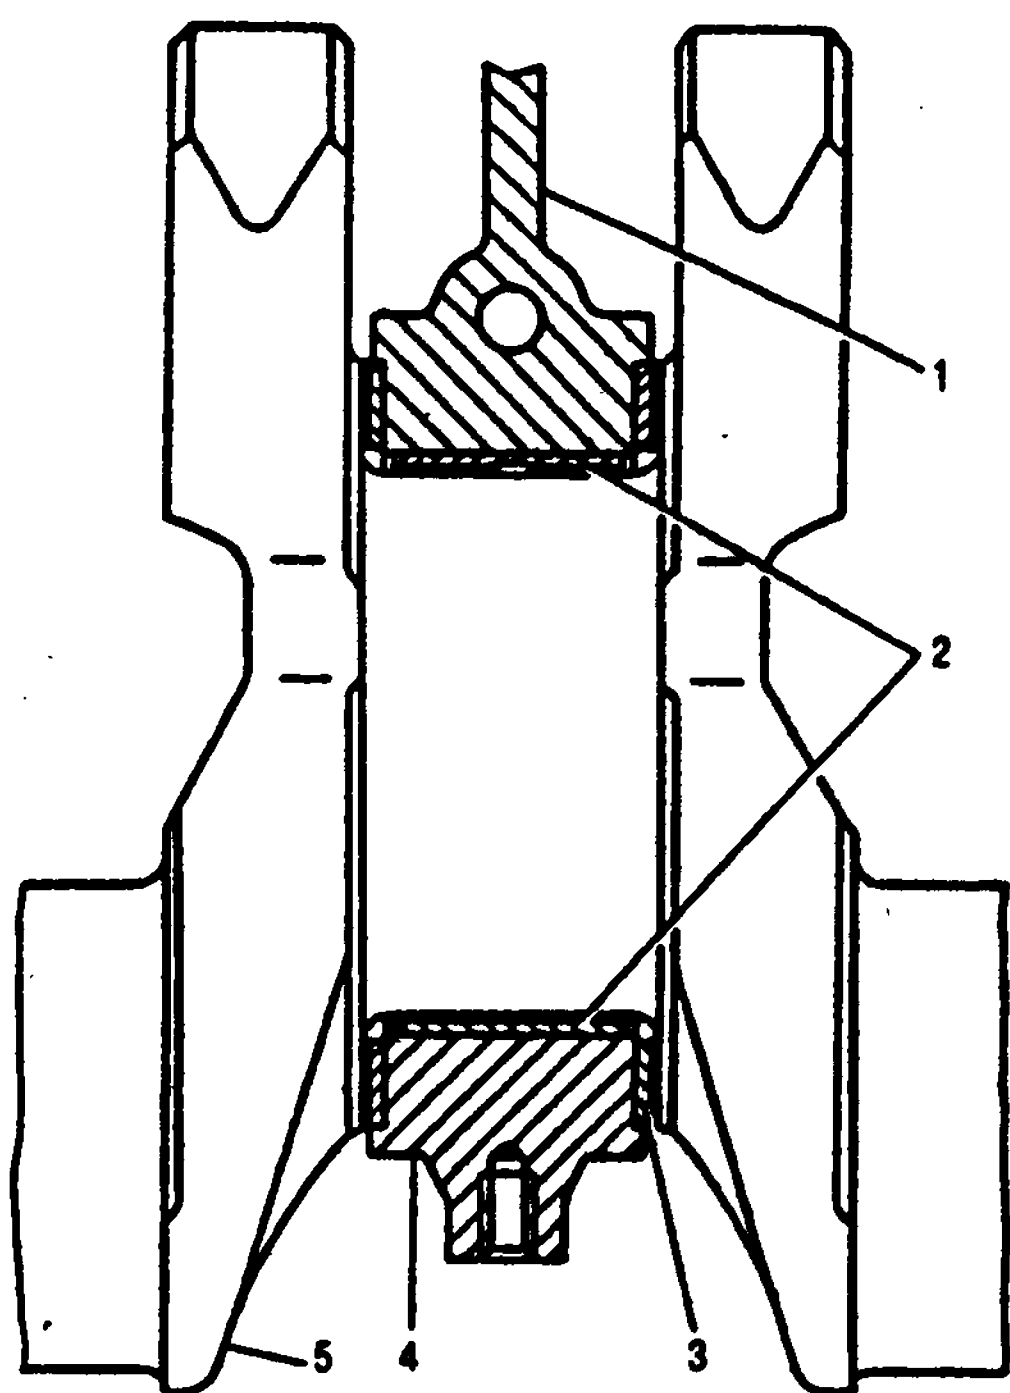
Средний (упорный) подшипник коленчатого вала: 1 - блок цилиндров; 2 - вкладыши подшипника; 3 - упорные полушайбы; 4 - крышка подшипника; 5 - коленчатый вал
